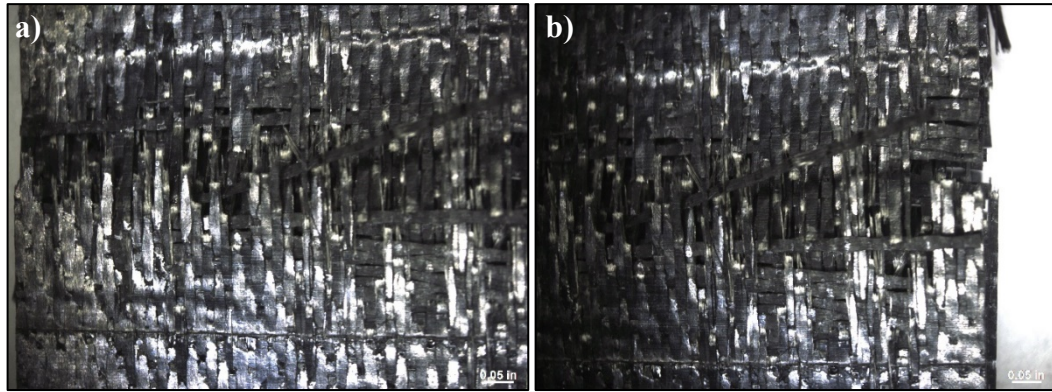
Inspección visual de probeta 2 de 5 capas a la falla, que presenta un código de falla AGM a) extremo izquierdo y b) extremo derecho de la probeta con fractura expuesta.
